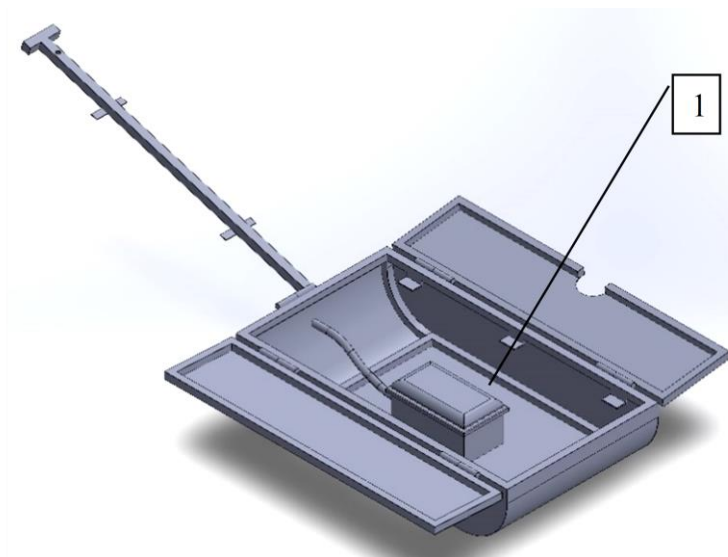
Общий вид корпуса МТВУ с установленным газовым обогревателем: 1 – установленный газовый обогреватель.
